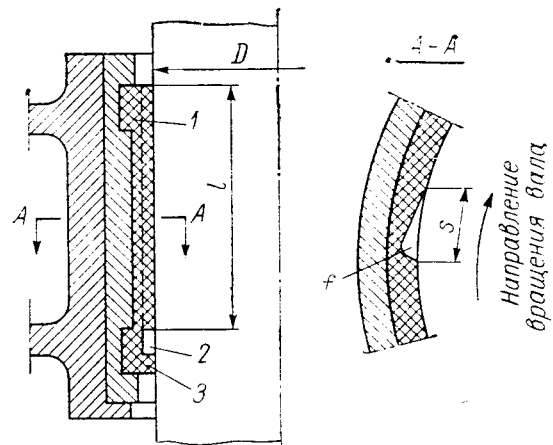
Резиновый подшипник в разрезе: 1 — резиновый вкладыш; 2 — кольцевая канавка; 3 — подпирющий пояс
